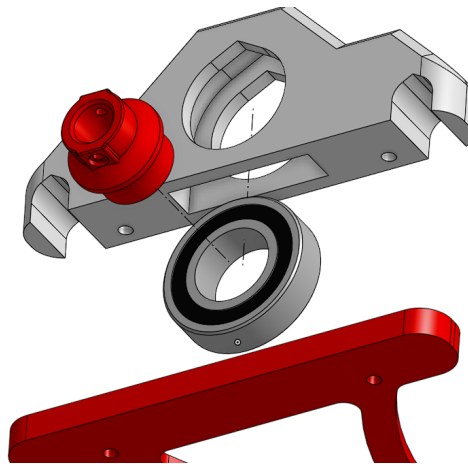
Vista explosionada 2 del ensamblaje de uno de los cojinetes del eje de rotación de la hélice en Onshape [fuente: elaboración propia]
